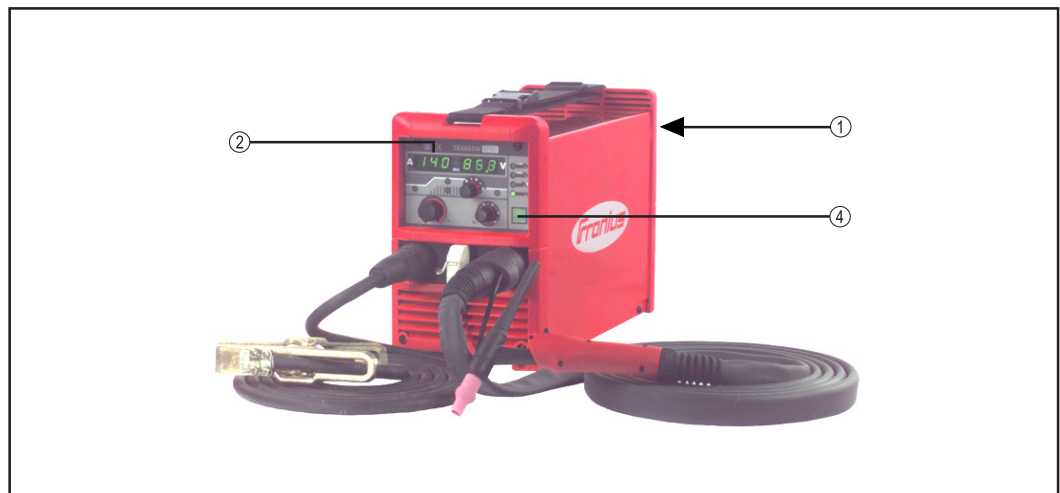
Transtig 1600/1700, como máquina de soldadura TIG, está formada por: fuente de potencia por bloque de mando, antorcha manual, cable de puesta a masa (botella de gas con manorreductor, sin figura)
